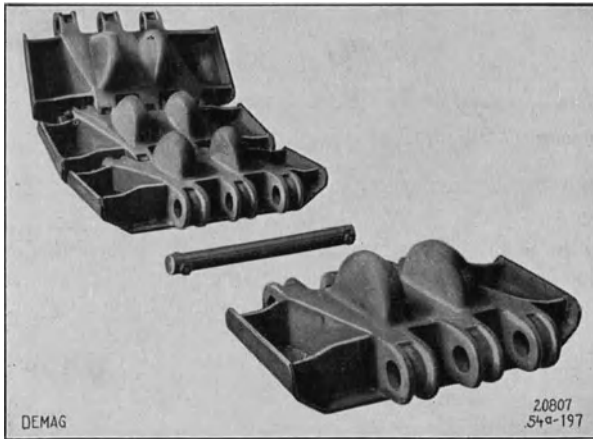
Aufgelöstes, geschweißtes Raupenglied (Demag).
